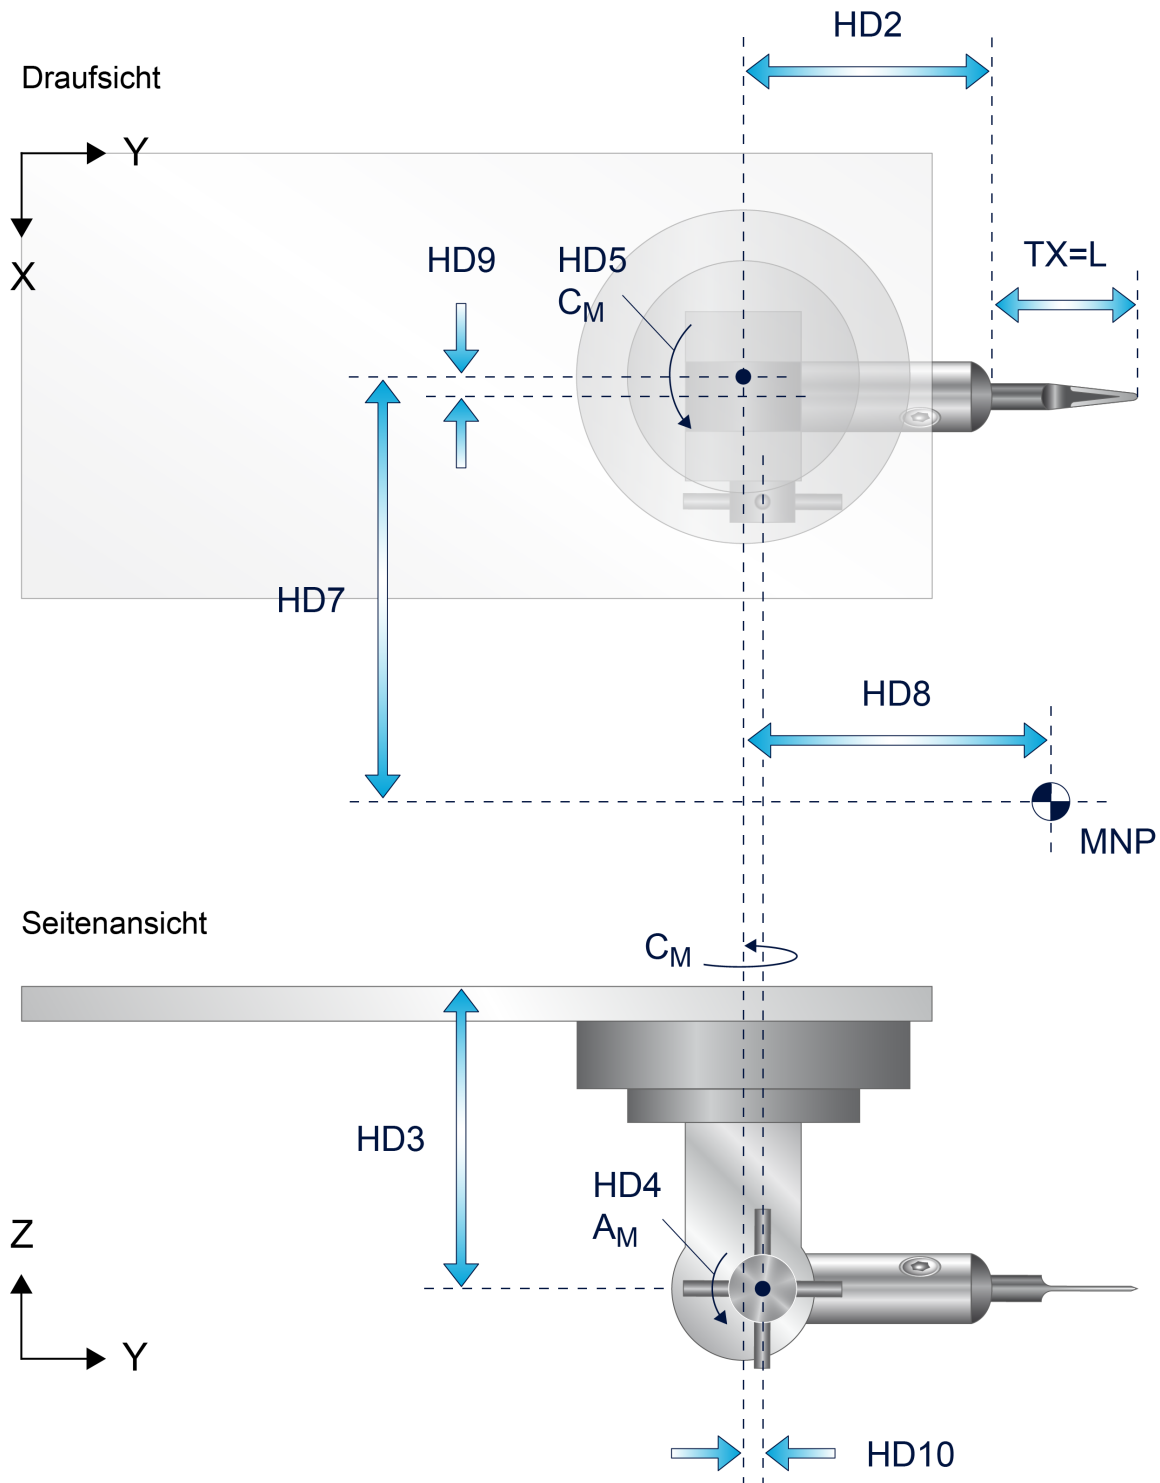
5-achsiges Schneidwerkzeug bei 90 Grad Winkelstellung
